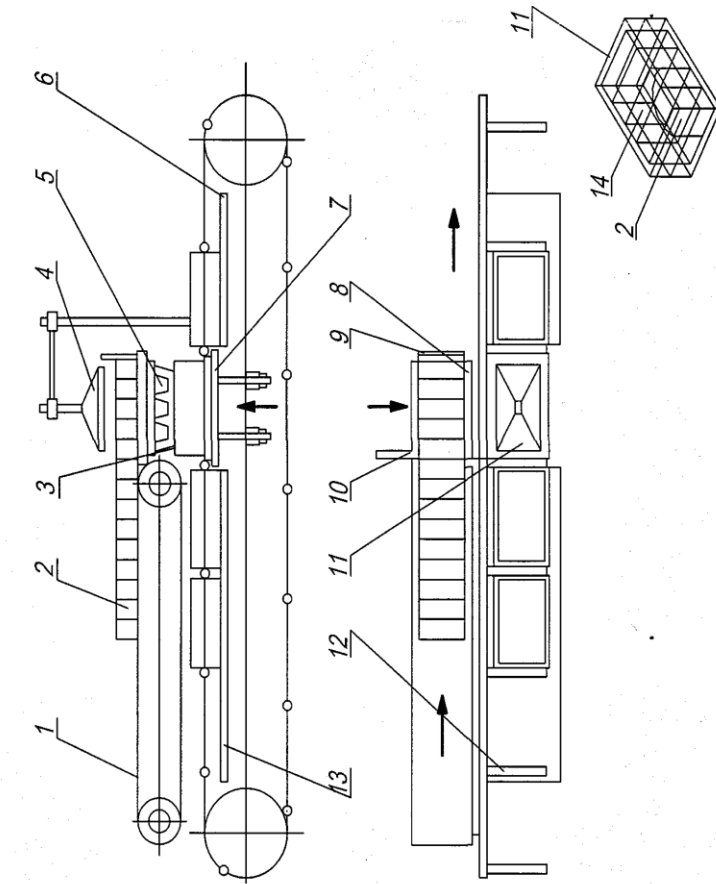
Схема пристрою для укладання в короби прямокутних коробок
